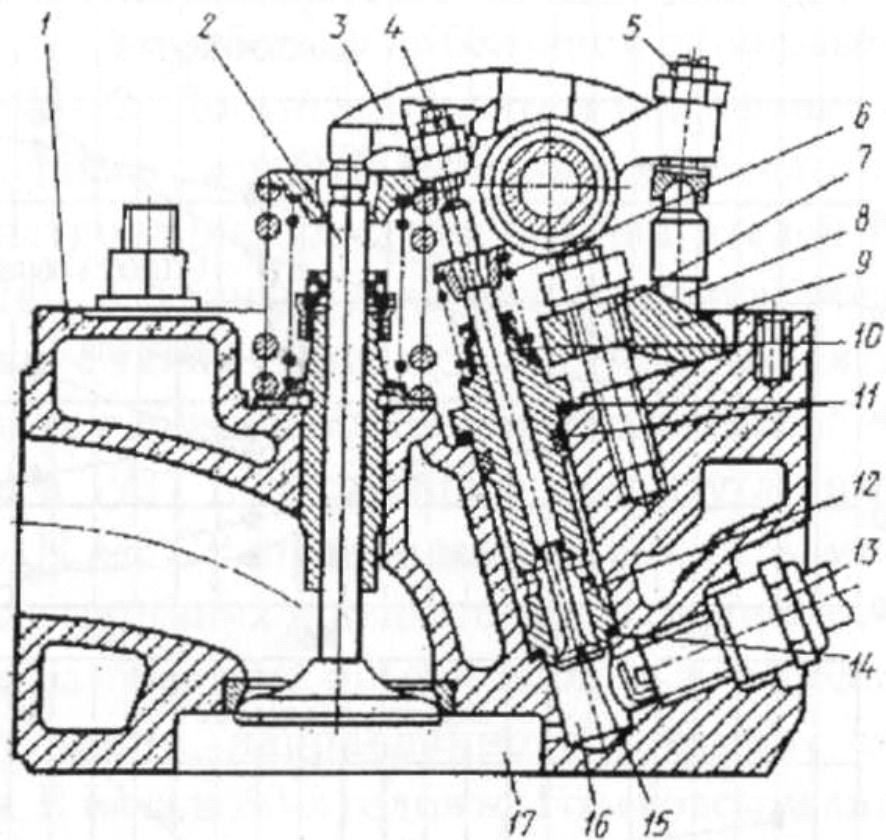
Привод клапанов форкамерного двигателя:
